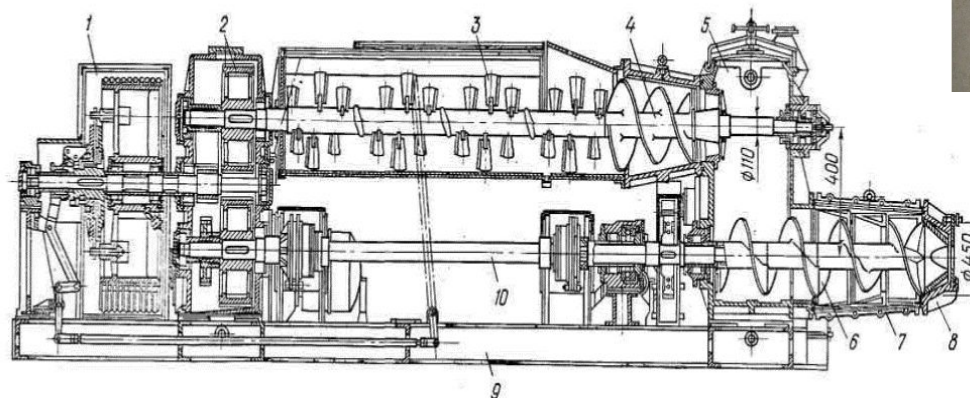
Ленточный вакуумный комбинированный пресс СМК-28 (СМ-443А):
